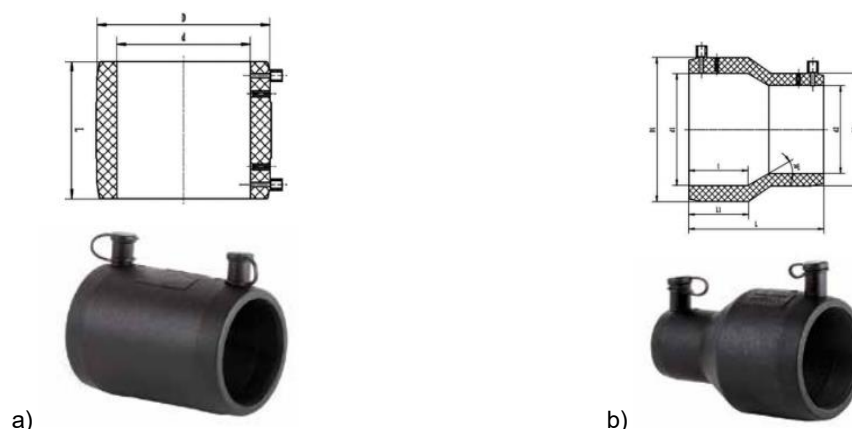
a) Manguito D1-D1 electrosoldable PE. b) Reductor D1-D2 electrosoldable PE. Fuente: www.egbgroupp.com
